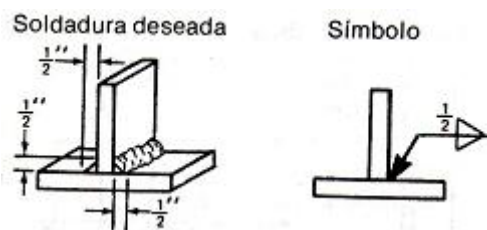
Símbolos de soldadura y las soldaduras representadas por ellos. (American Welding Society, Welding Handbook, 6ª. Ed., 1963, sección 1, p. 1.50.).
